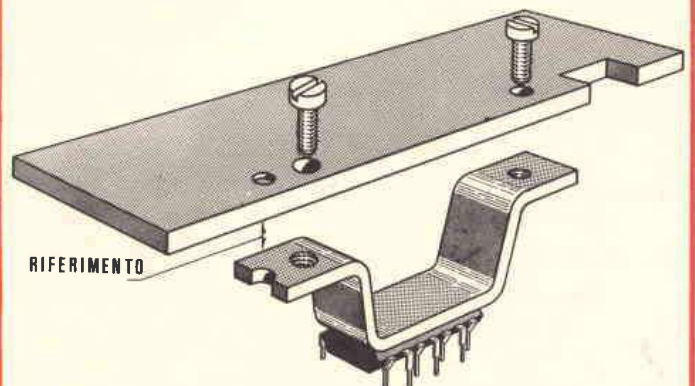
Montaggio del circuito integrato TAA 611/C.
